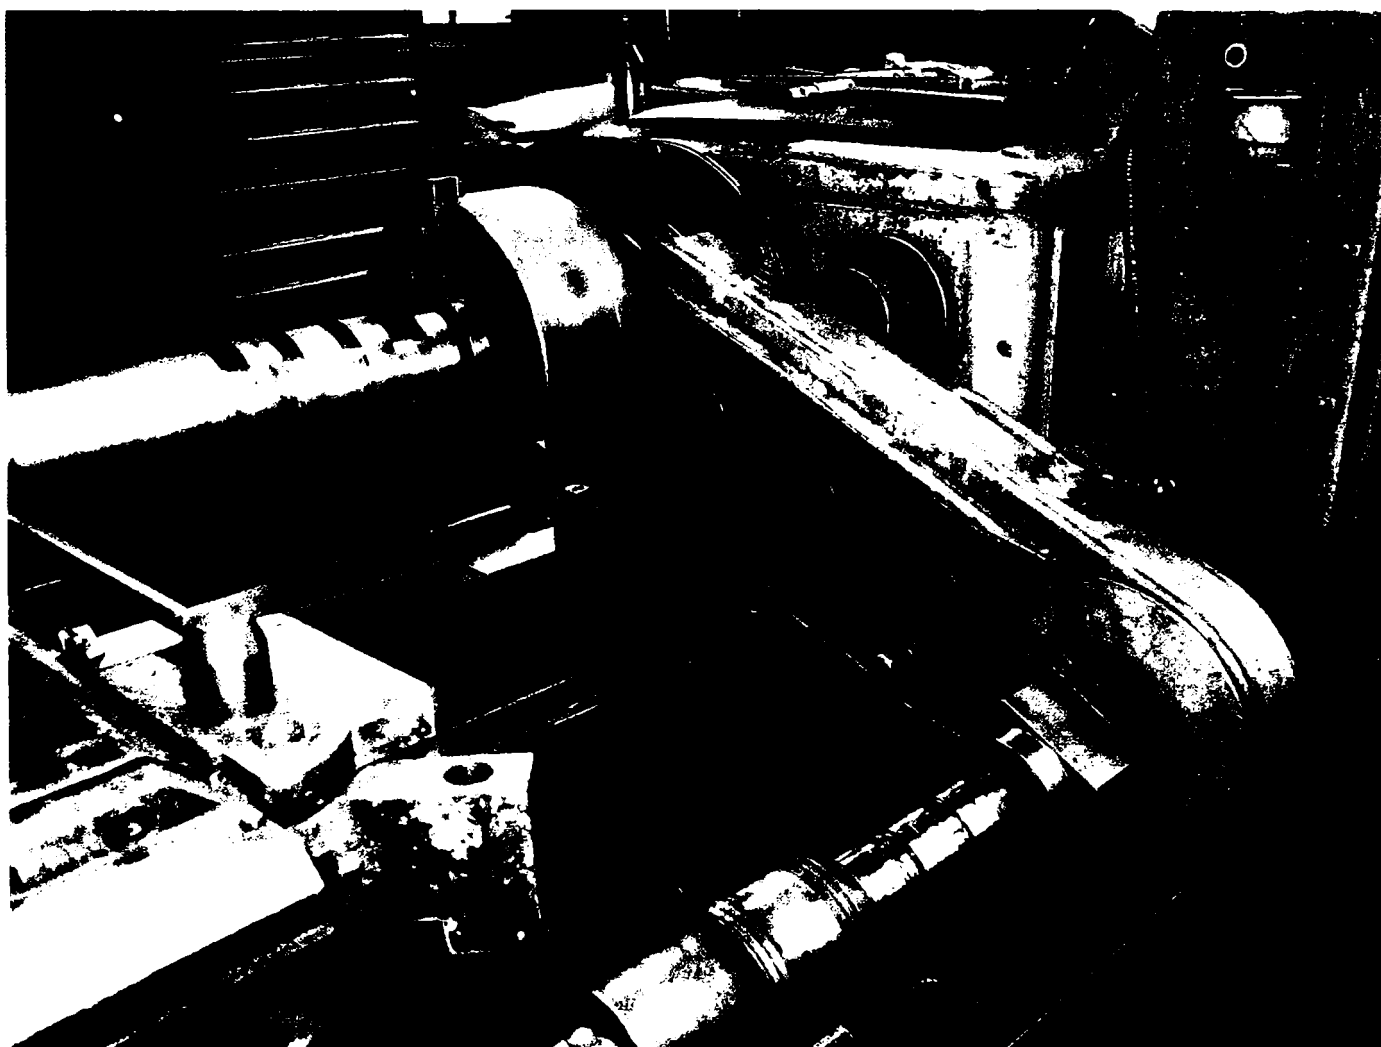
Adaptarea strungului 1 M 63 pentru strunjirea prin copiere a profilului camelor
